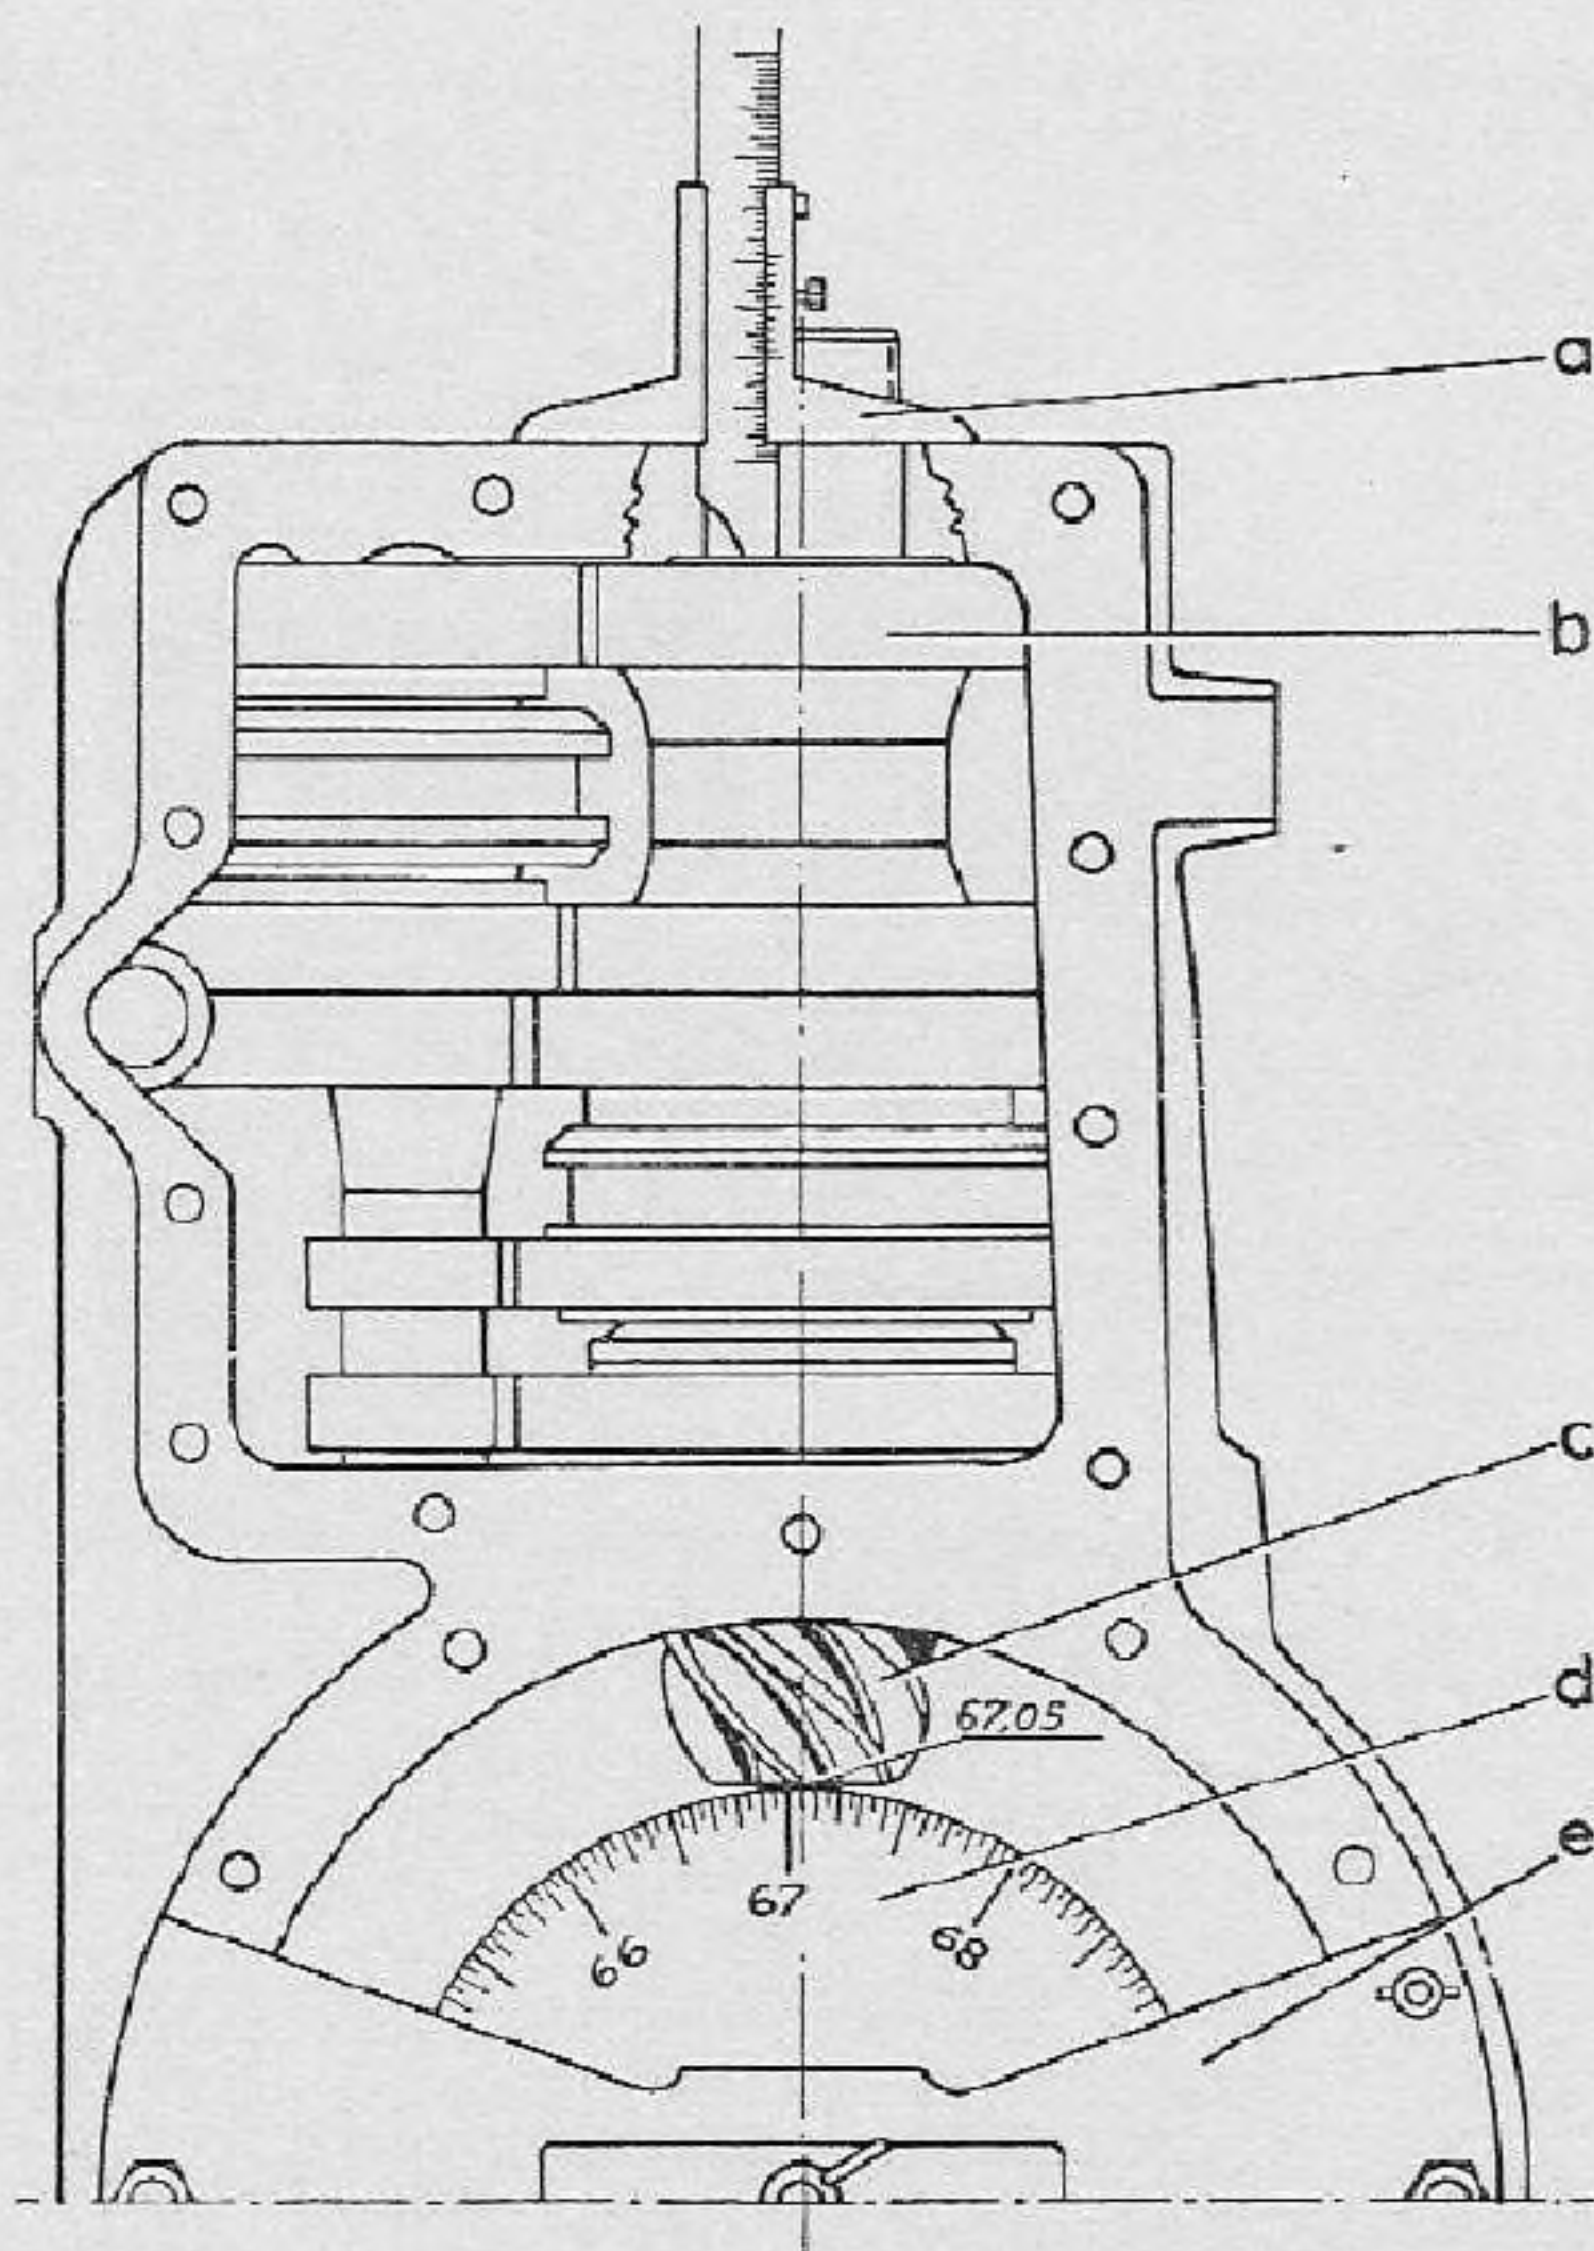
Determinación del espesor de la arandela compensadora del engranaje de 4ª.
